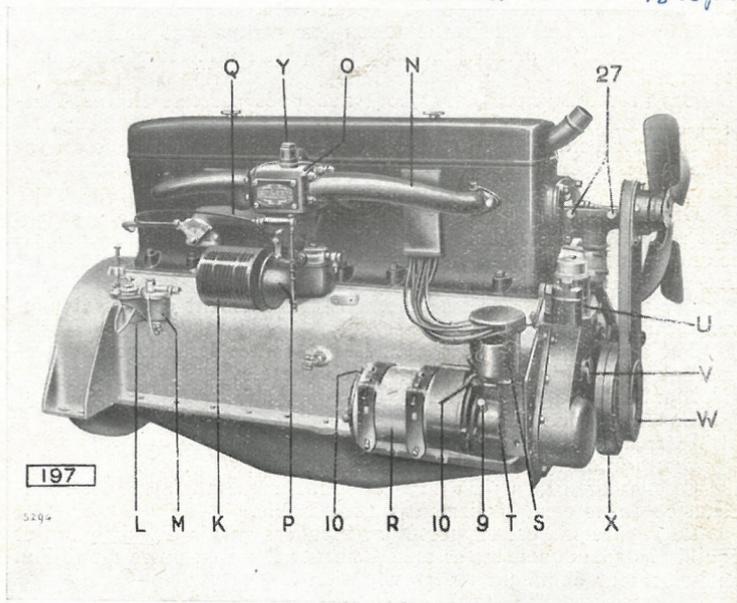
MOTEUR. — VUE COTE CARBURATEUR
